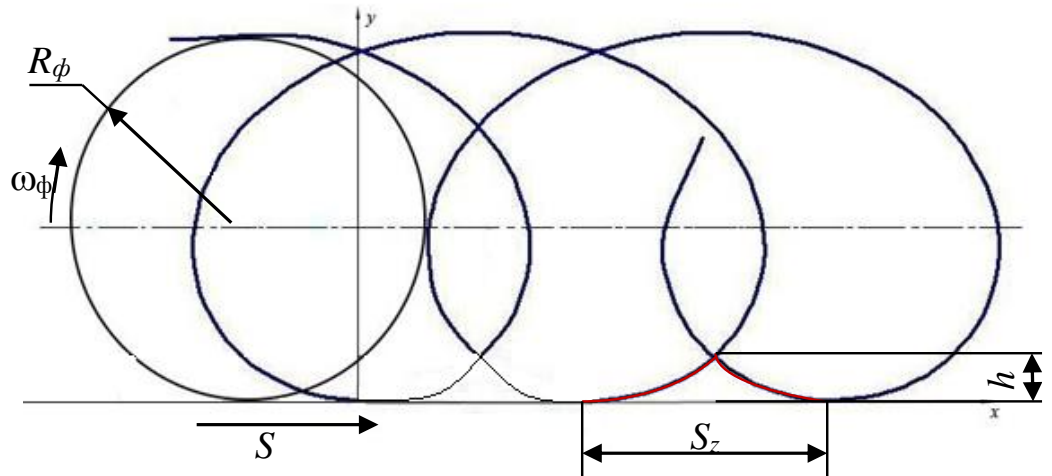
Визначення висоти гребінця для попутного фрезерування плоских поверхонь
